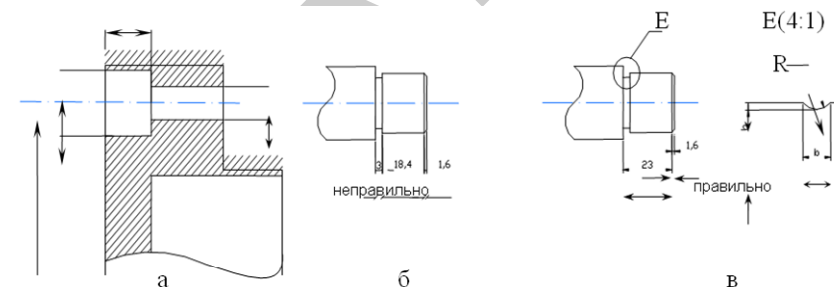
Примеры нанесения размеров на чертежах: а — нанесение размеров одного конструктивного элемента; б — ошибочное обозначение ширины канавки; в — правильно указанная ширина канавки
